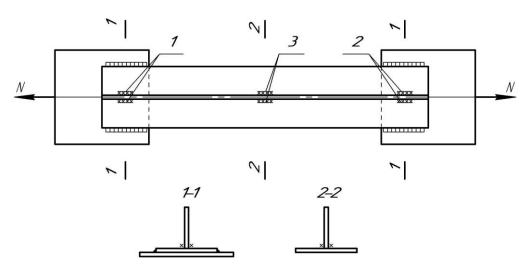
К вопросу о порядке наплавки сварных швов
